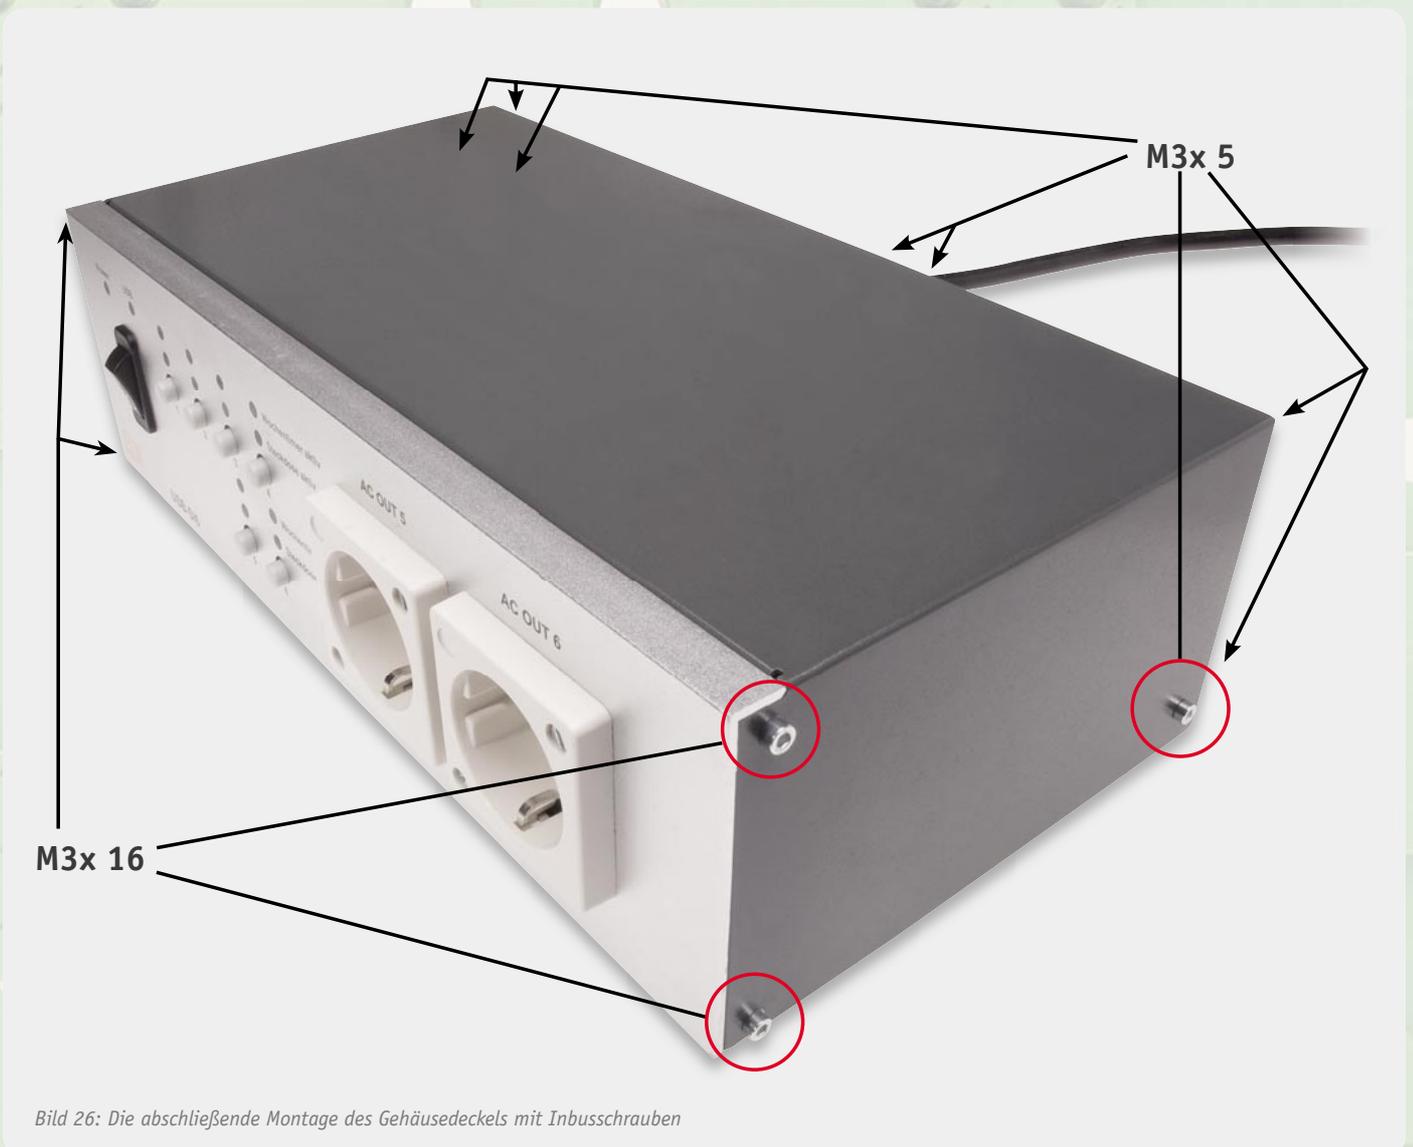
Die abschließende Montage des Gehäusedeckels mit Inbusschrauben
